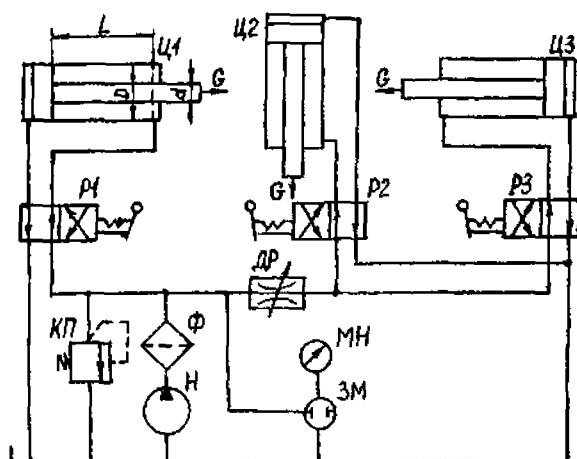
Гидравлическая схема запрессовочного приспособления
